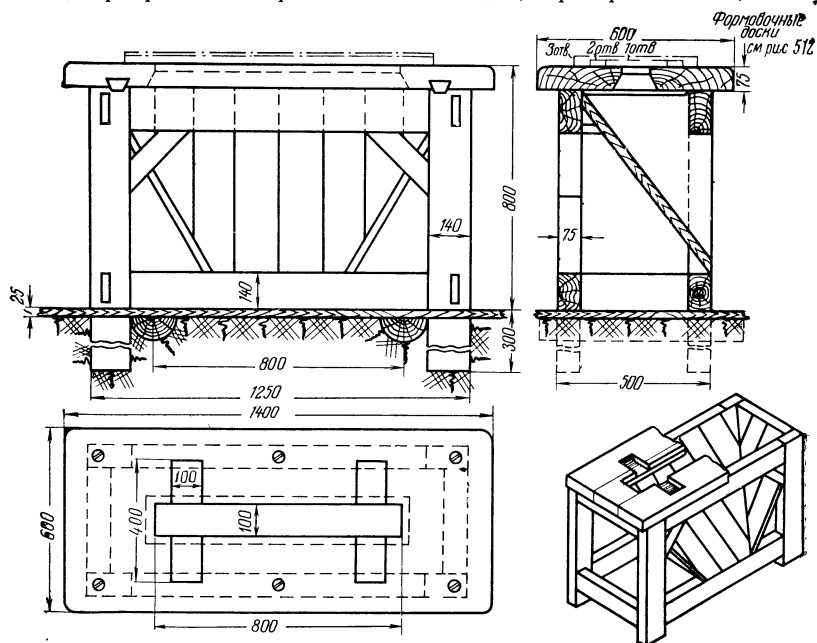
Деревянный стол (станок) для изготовления бетонных труб
